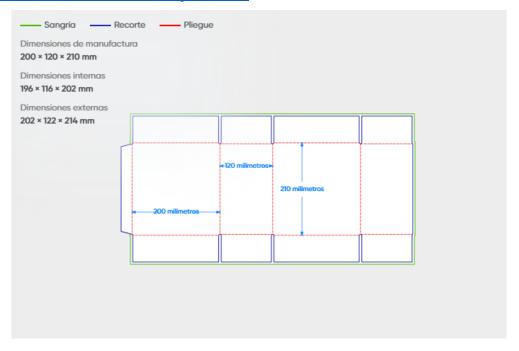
Dimensiones del troquelado del empaque para Quick & Clean.
